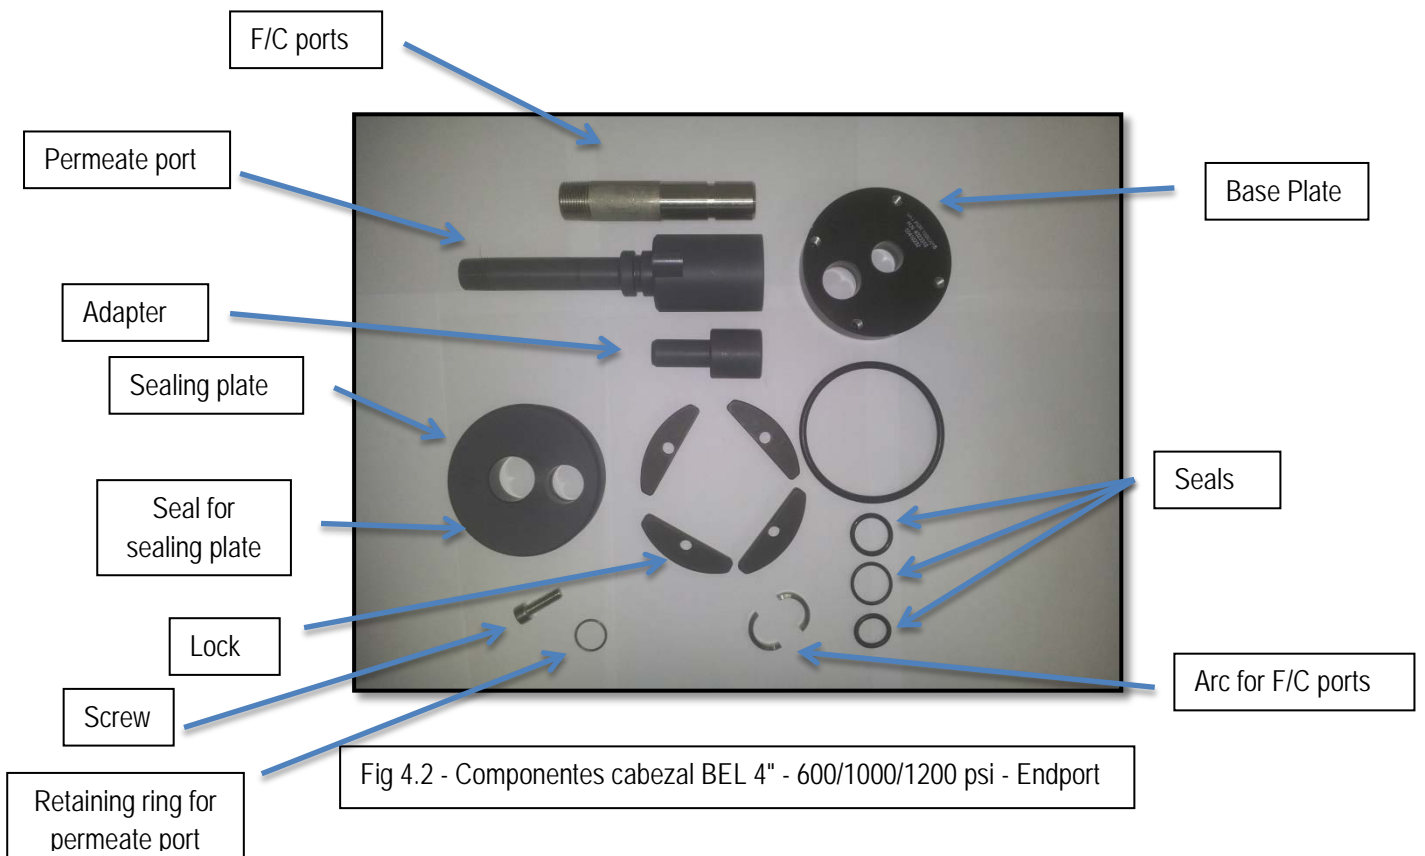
Componentes cabezal BEL 4" - 600/1000/1200 psi - Endport
